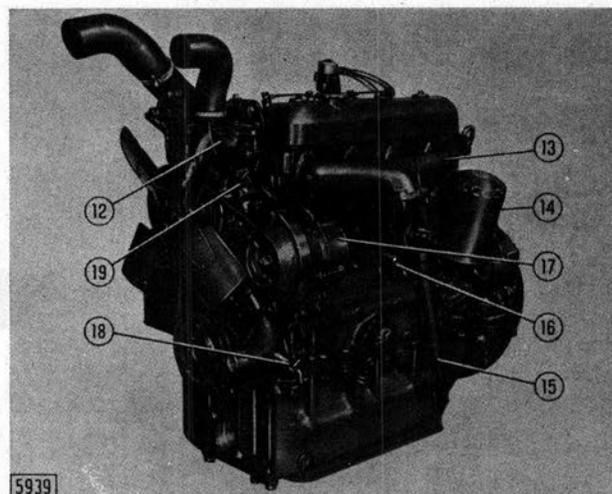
/1 - Vue de 3/4 avant gauche du moteur.
